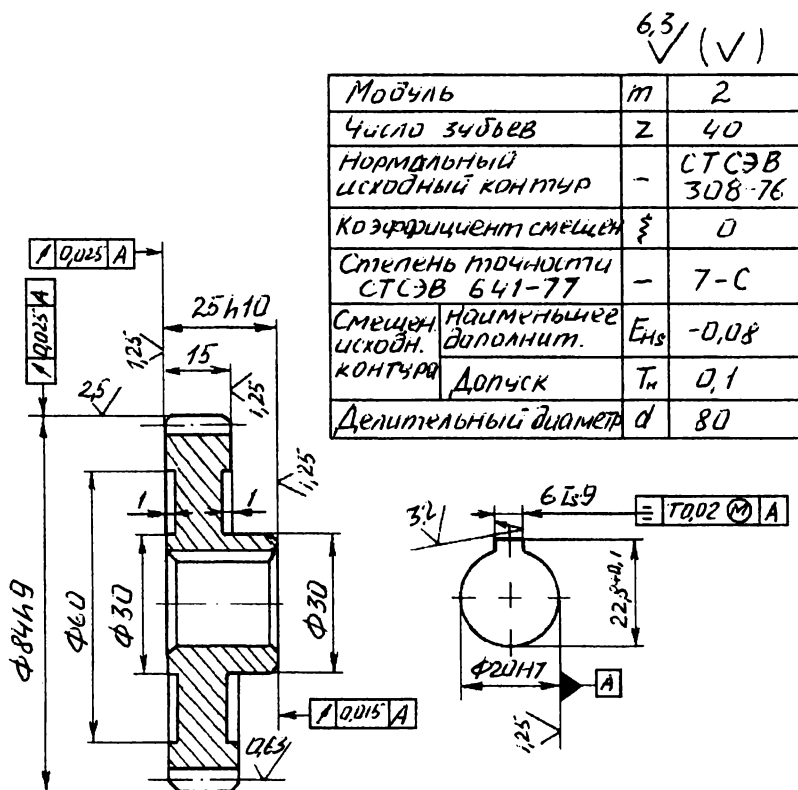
Пример оформления чертежа детали "Колесо зубчатое"
